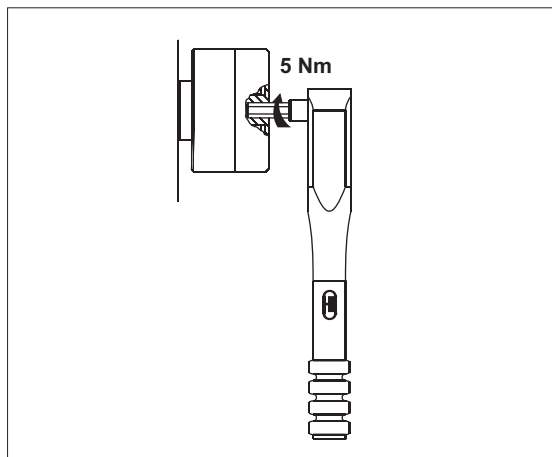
Затягивание винта крышки корпуса при помощи динамометрического ключа
